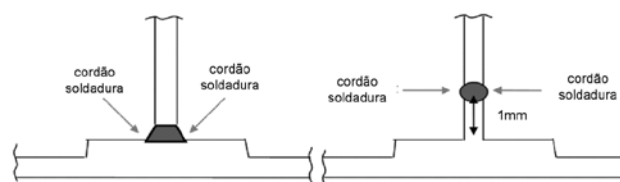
Configurações da soldadura nos provetes LBW.
